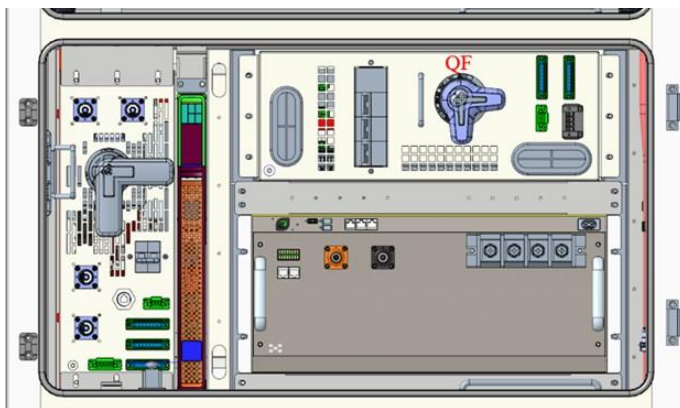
Desconecte manualmente o disjuntor moldado QF
